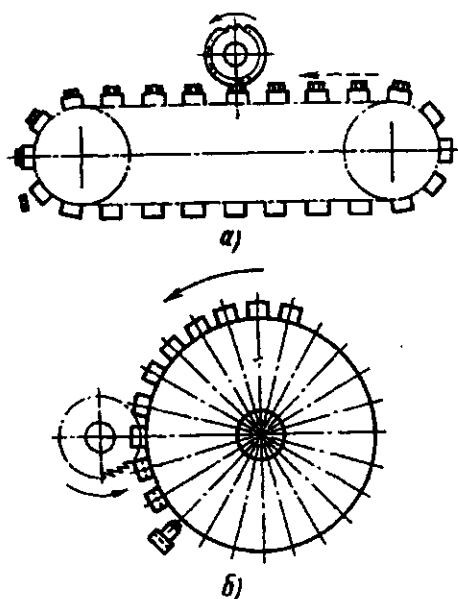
Приспособление к горизонтально-фрезерному станку: а – конвейерного типа; б – барабанного типа
